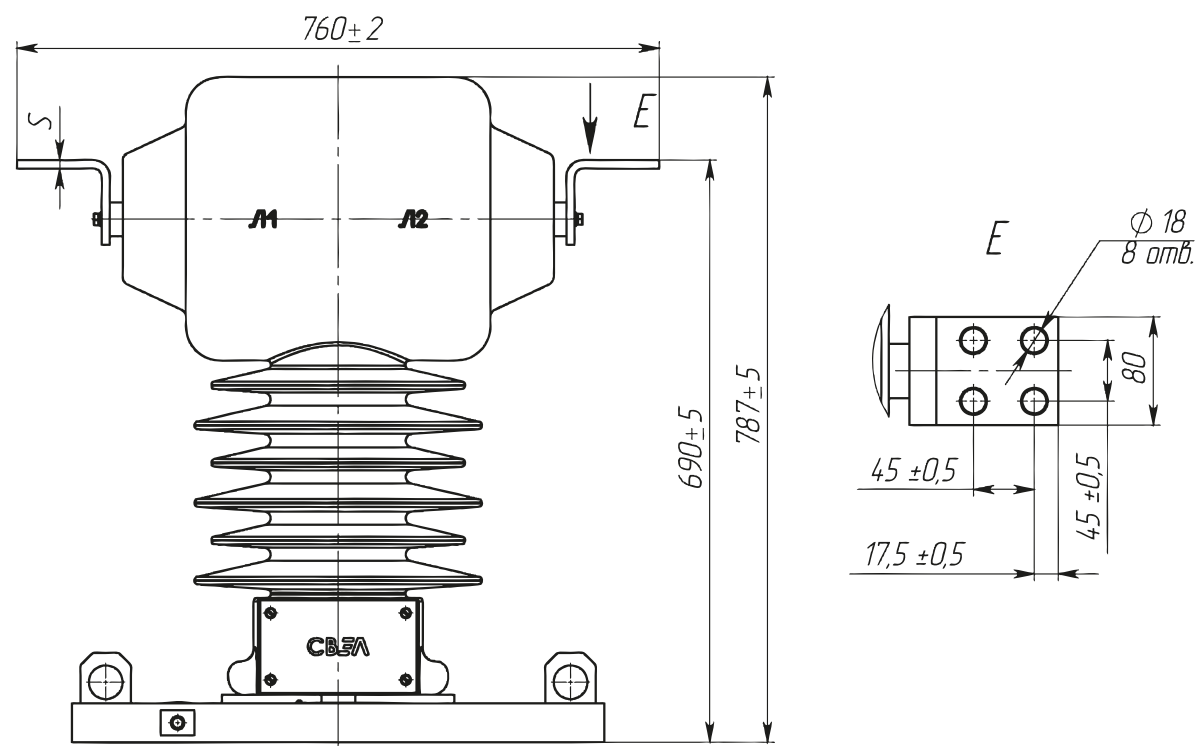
Общий вид трансформатора ТОЛ-СВЭЛ-35 III на номинальный первичный ток 2500, 3000А
